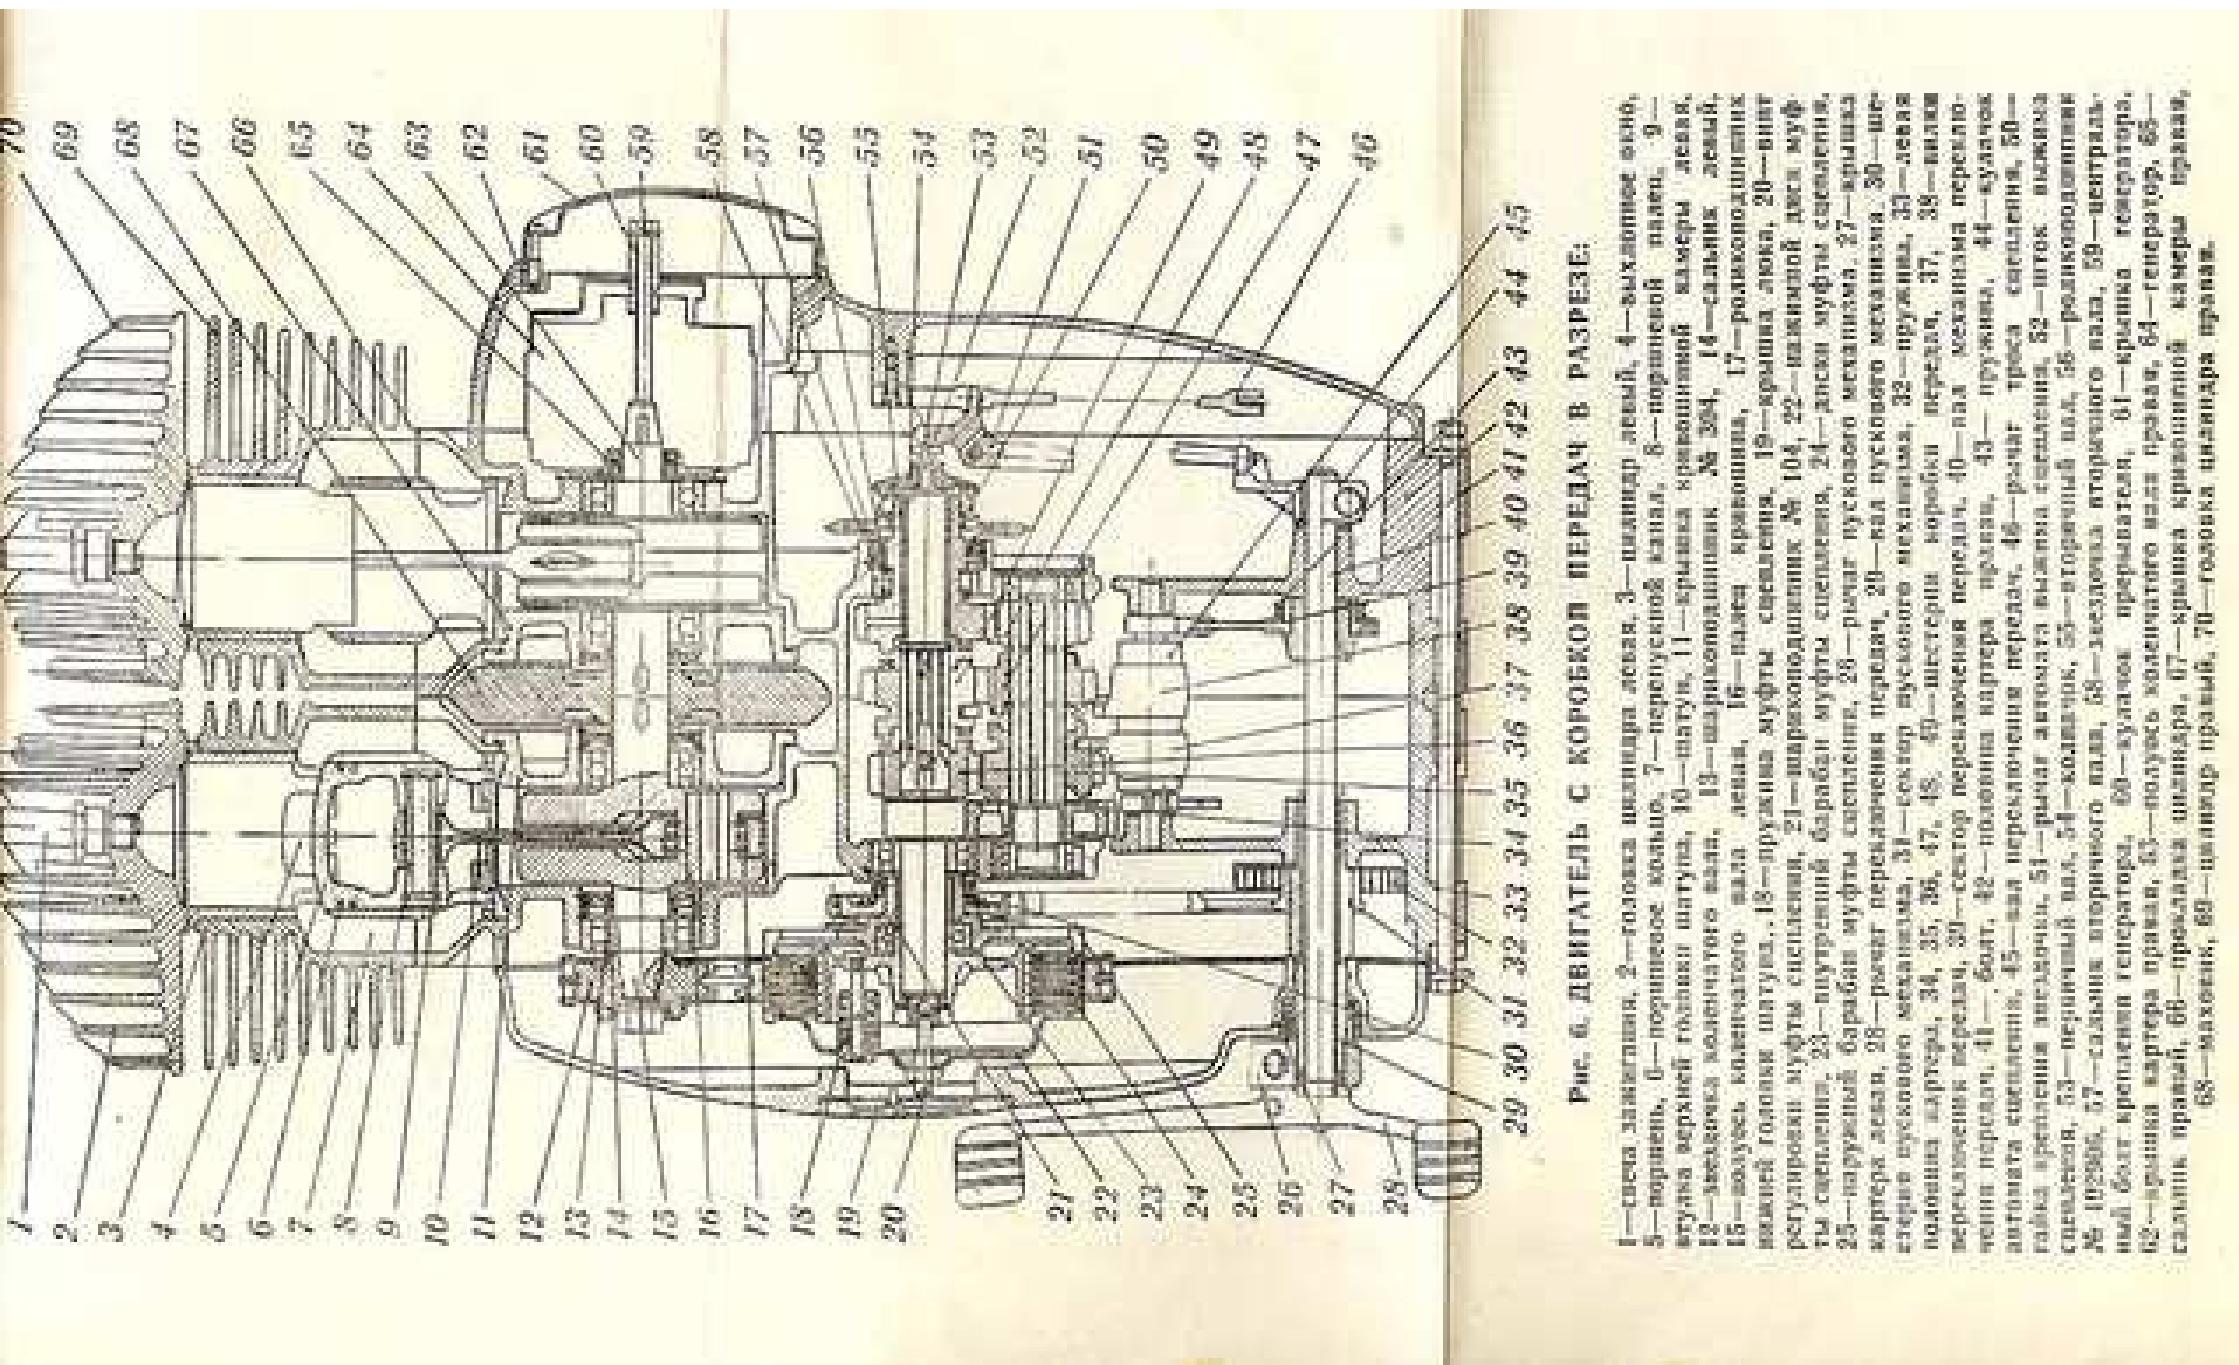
ДВИГАТЕЛЬ С КОРОВКОЙ ПНЕВМЫ В РАЗРЕЗЕ.
